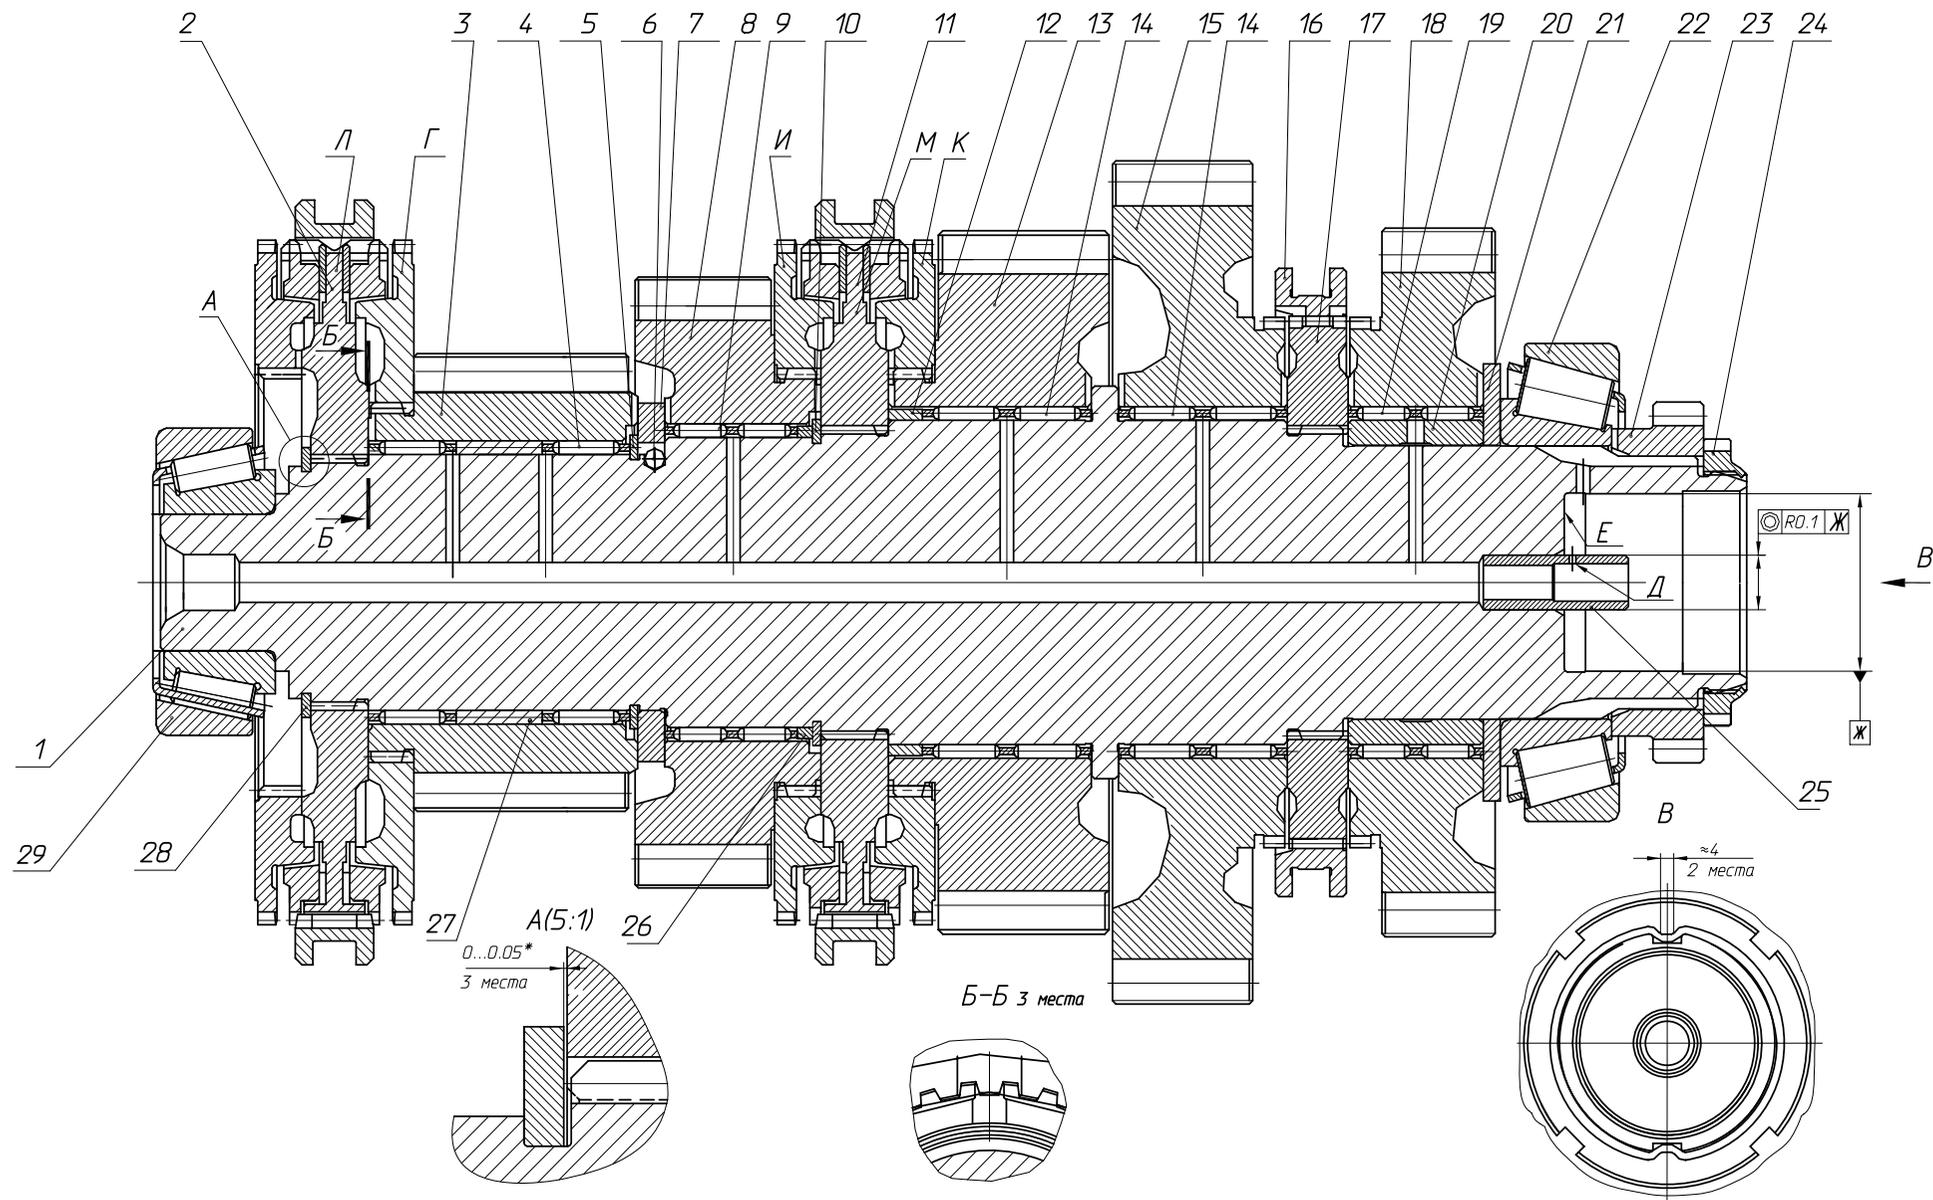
Устройство вала вторичного в сборе дет. 239.1701100 КП ЯМЗ-239
